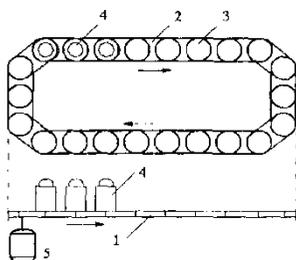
Схема пластинчатого транспортера: 1 - приводная цепь с пластинами; 2 - пластина типа; 3 - пластина типа; 4 - перемещаемый предмет; 5 - привод
